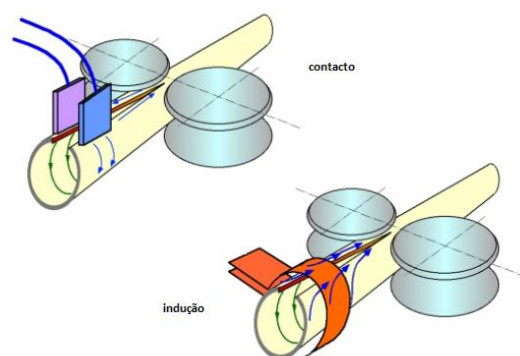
Soldadura por resistência elétrica de alta frequência de contacto (cima) e indução (baixo) [9]
